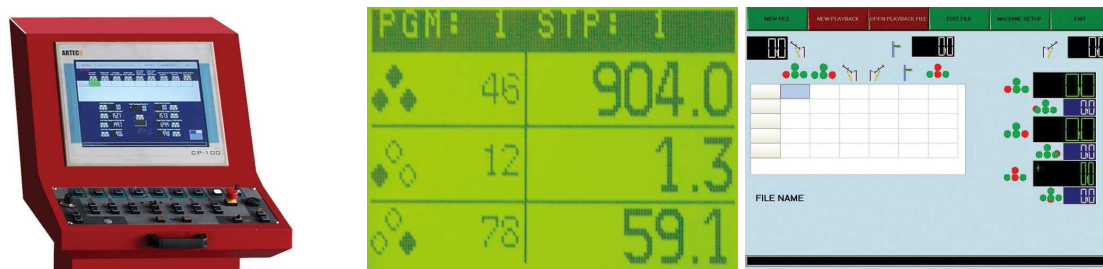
Automatizované zařízení s dvouválcovou zakružovačkou [23]
